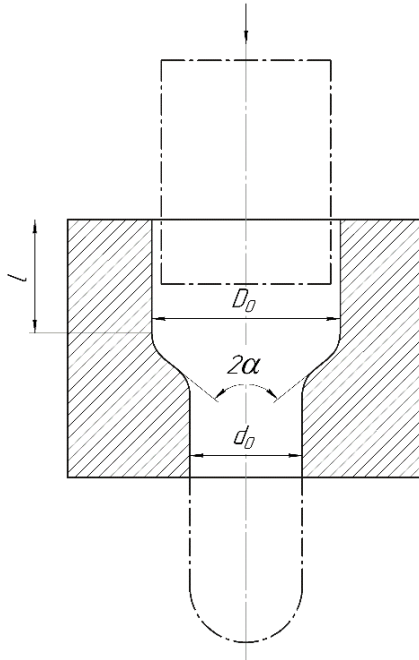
Круглая матрица для штамповки поковок прямым выдавливанием
